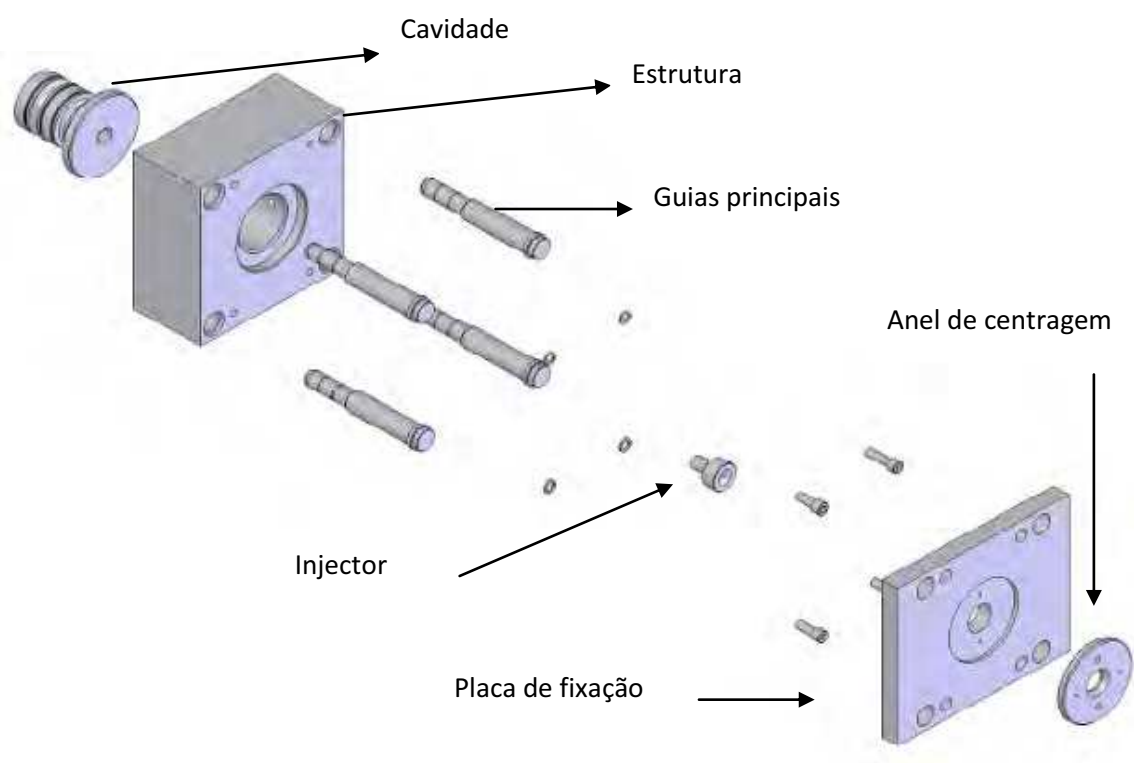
Vista 3D explodida dos componentes do molde - parte de injeção
